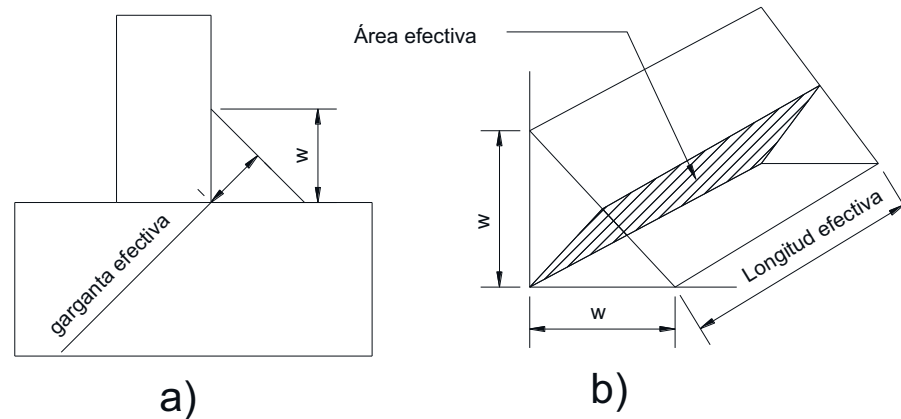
Área efectiva para soldaduras de filete
